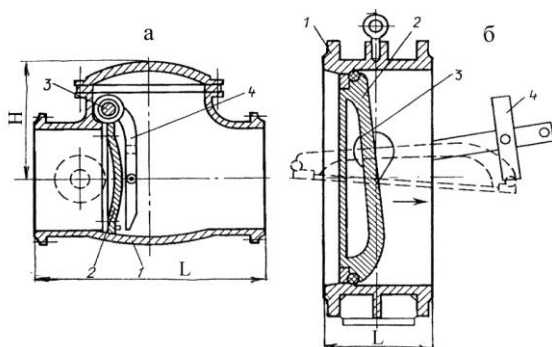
Обратный клапан: а – с верхней подвеской диска; б – с эксцентрично расположенной осью; 1 – корпус; 2 – тарель; 3 – ось; 4 – рычаг
